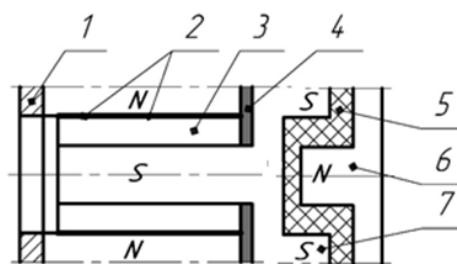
Развертка полюсной системы ротора БСГКВ по рис. 4 по поверхности расточки в пределах двух полюсных делений: 1 – униполярная пластина; 2 – сварочные швы; 3 – немагнитная вставка обода (наружного цилиндра); 4 – немагнитная заливка; 5 – сварка немагнитной сталью; 6 – внешняя полюсная группа магнитной системы регулировочного звена; 7 – внутренняя полюсная группа магнитной системы регулировочного звена
